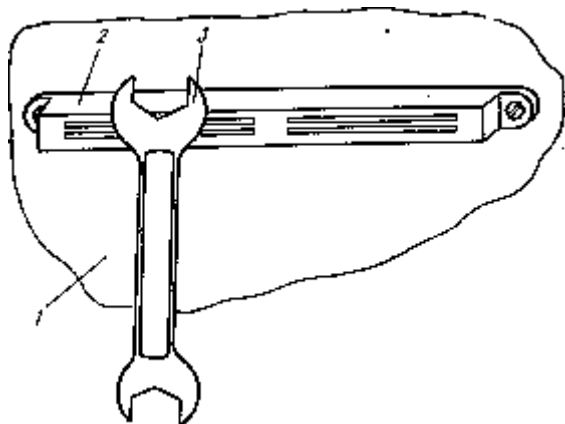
Магнитный держатель для инструмента: 1 — доска для инструмента; 2 — магнитная планка; 3 — инструмент
